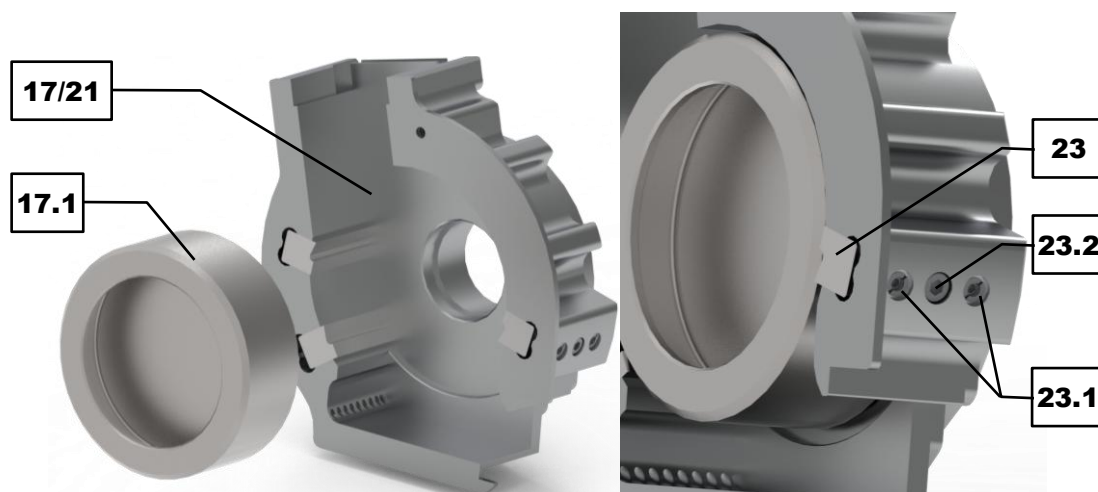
Установка приспособления для настройки и регулировка режущих брусков
